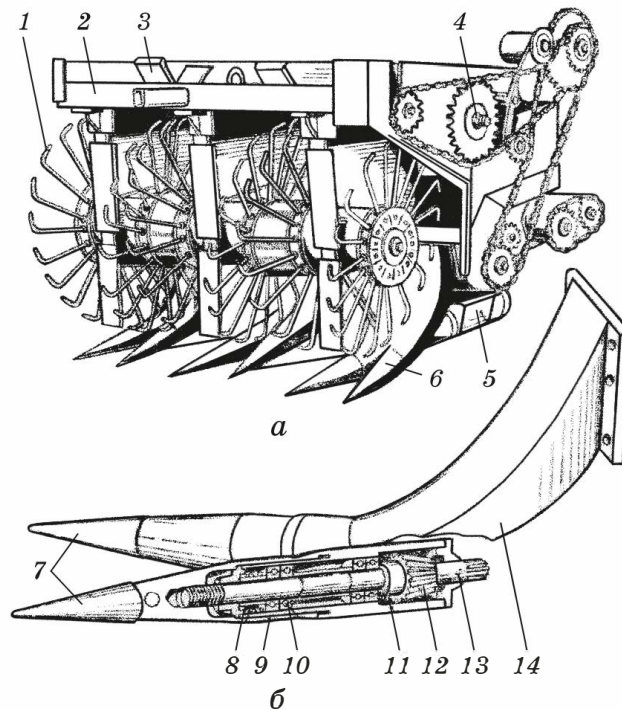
Викопувальний пристрій коренезбиральної машини МКК-6-02:
